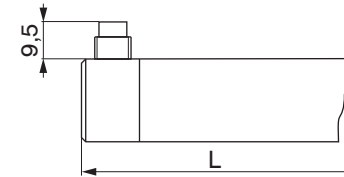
Wegsensor Typ - SR mit radialer Steckverbindung
